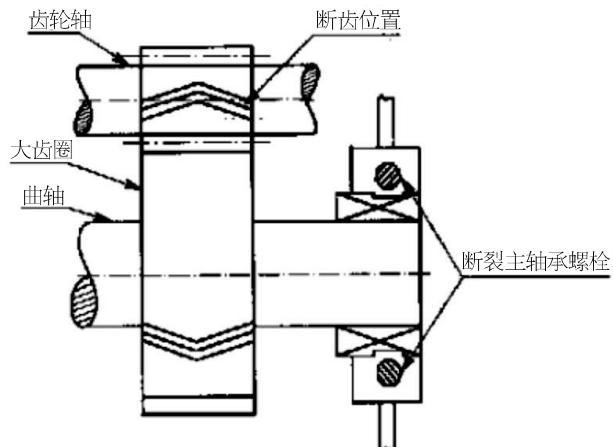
断裂的主轴承螺栓、齿轮轴、大齿圈相对位置示意图
